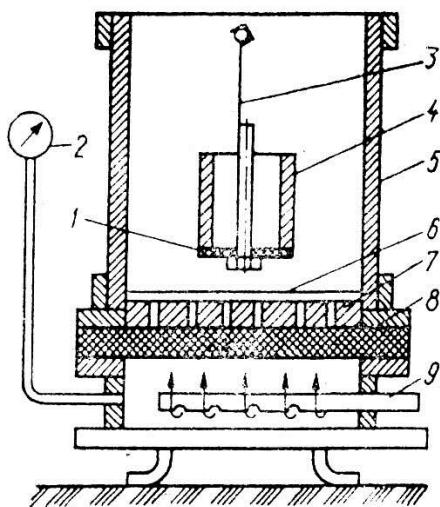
Схема вихорового напилення полімерного порошку:
